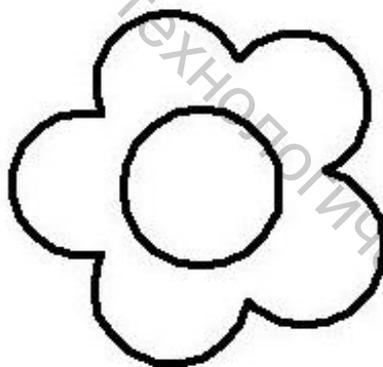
Пришиваемый элемент заготовки верха обуви
